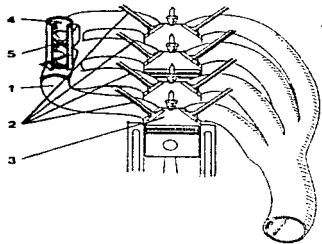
Esquema que muestra la disposición de un carburador en un motor.
